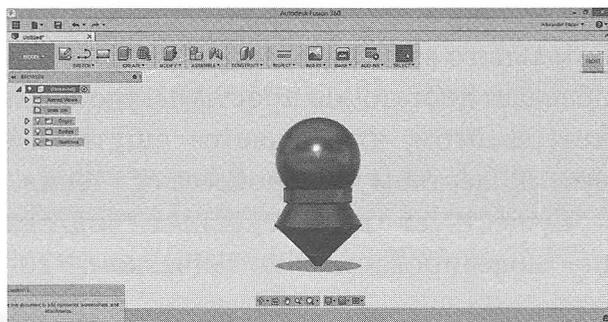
Объемная заготовка для модели корабля «Восток»
